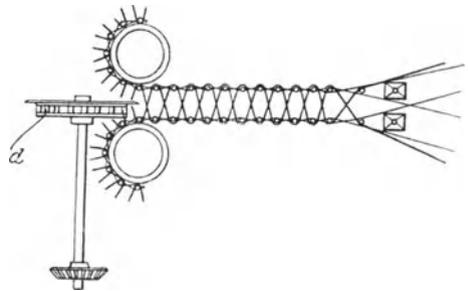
Schneidzeug mit auf einer endlosen umlaufenden Kette befestigten Messern.
